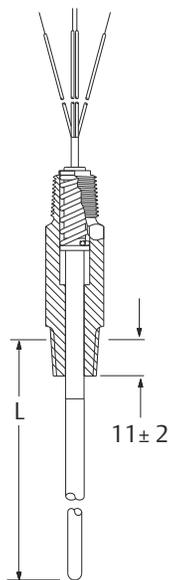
Montage sur tube universel avec Rosemount 3144P
